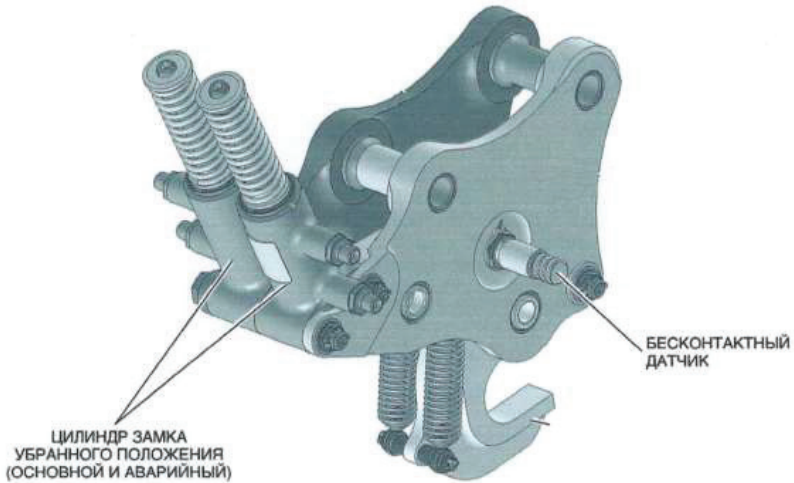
Замок убранного положения опоры шасси с резервированием гидроцилиндра управления положением зева
